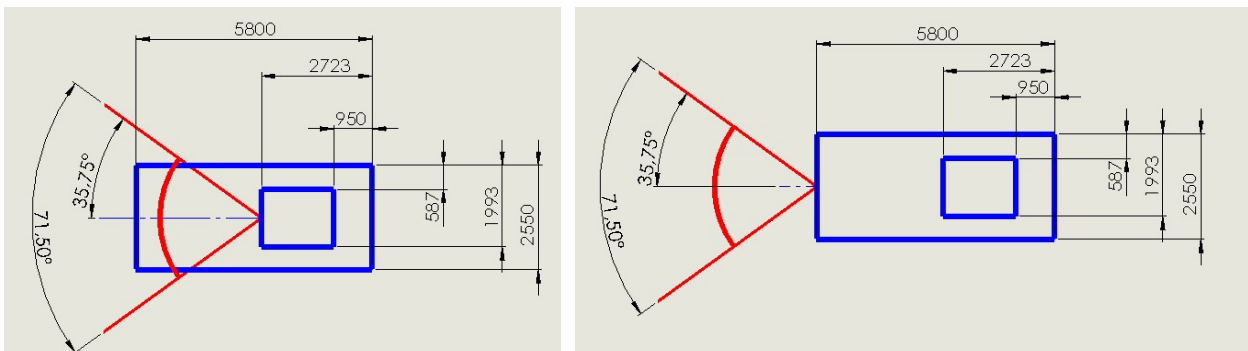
Vista Planta - Campo de visión de cámaras frontales
